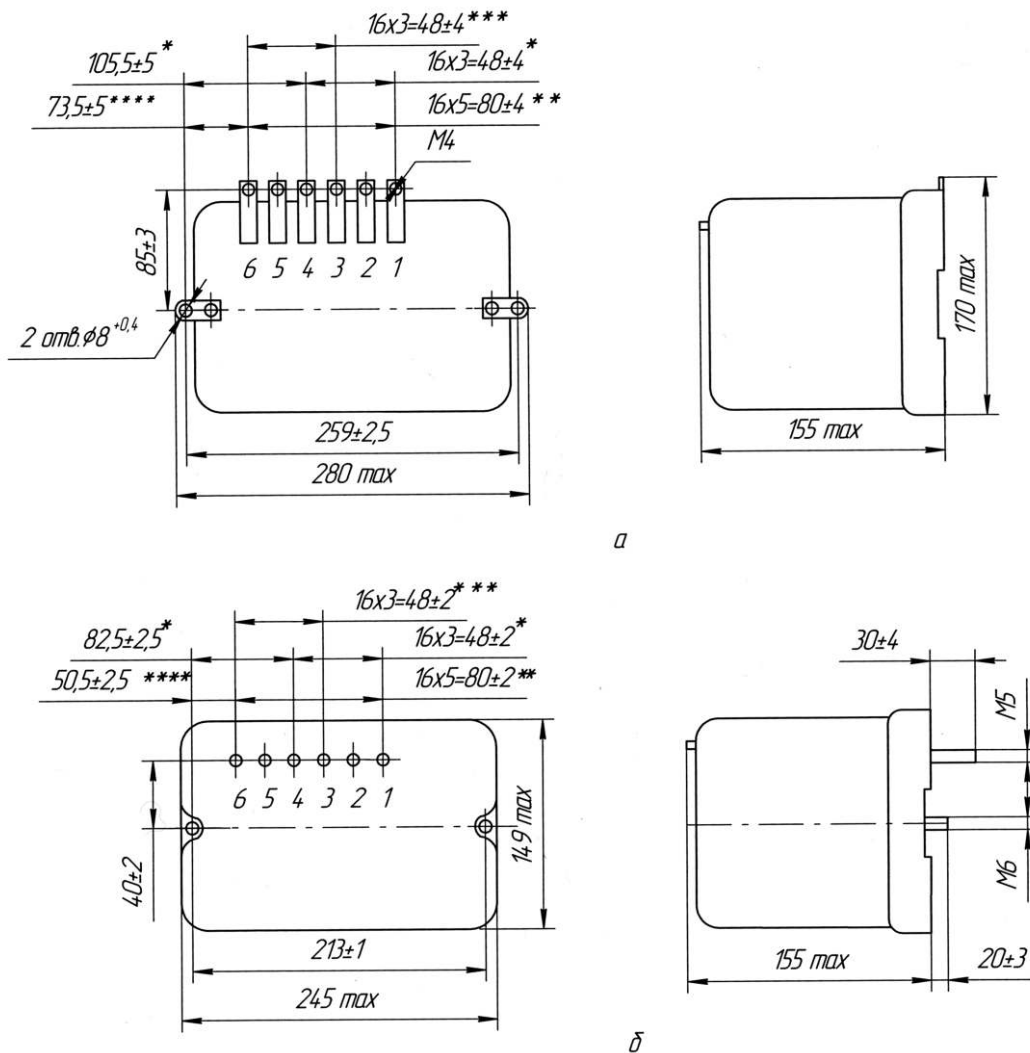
Габаритные, установочные, присоединительные размеры реле серии РТ-80, РТ-90:
